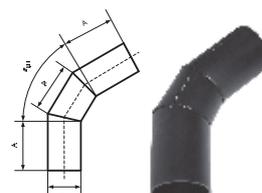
Отвод 60° сварной 3-х сегментный
